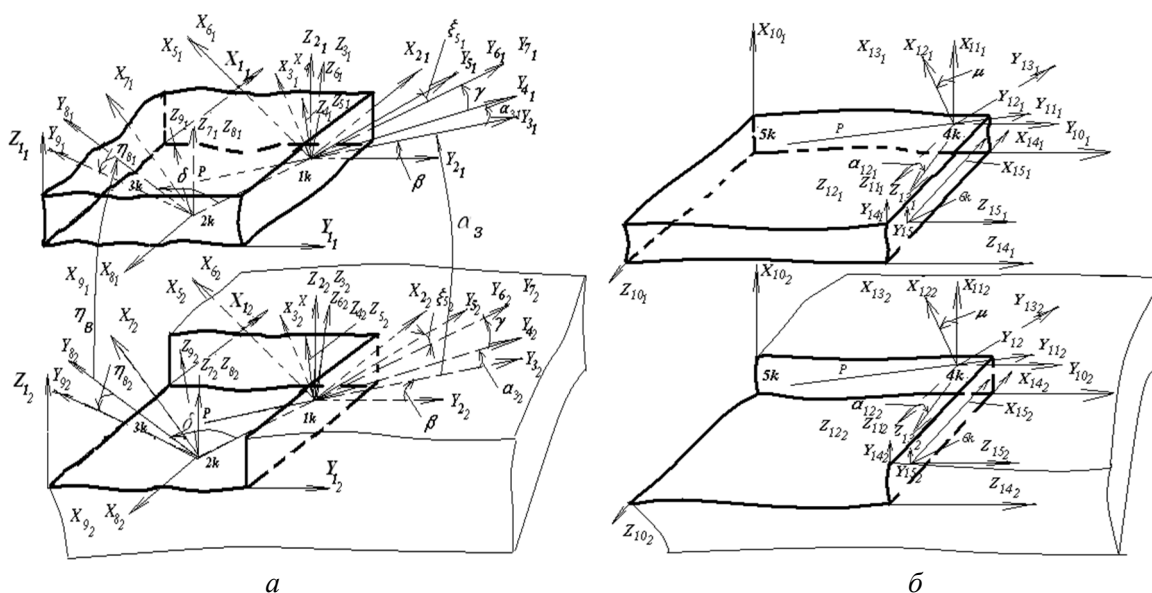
Схема к расчету координат точек контакта СМП и паза корпуса инструмента: а – для опорной поверхности; б – для боковых поверхностей
